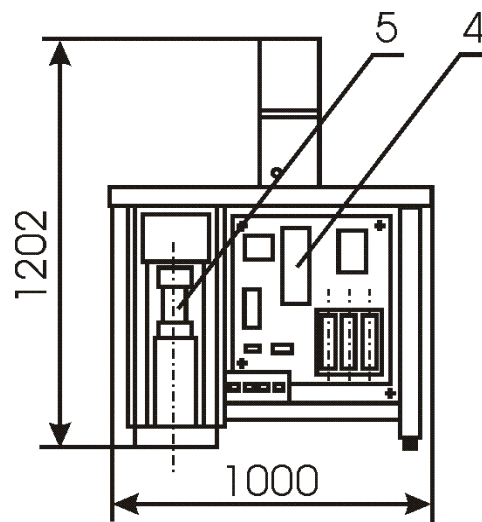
Установка сварки, резки и термообработки (вид сзади)
